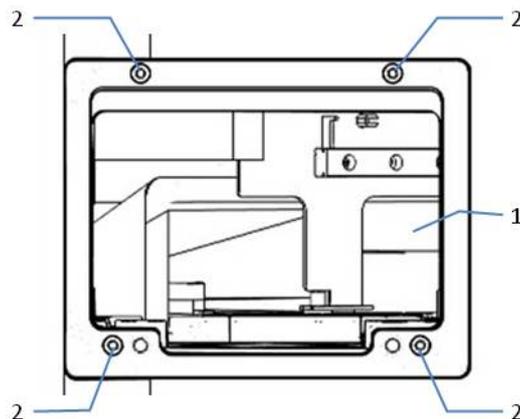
Schrauben zur Befestigung des Chargers am Autosampler
